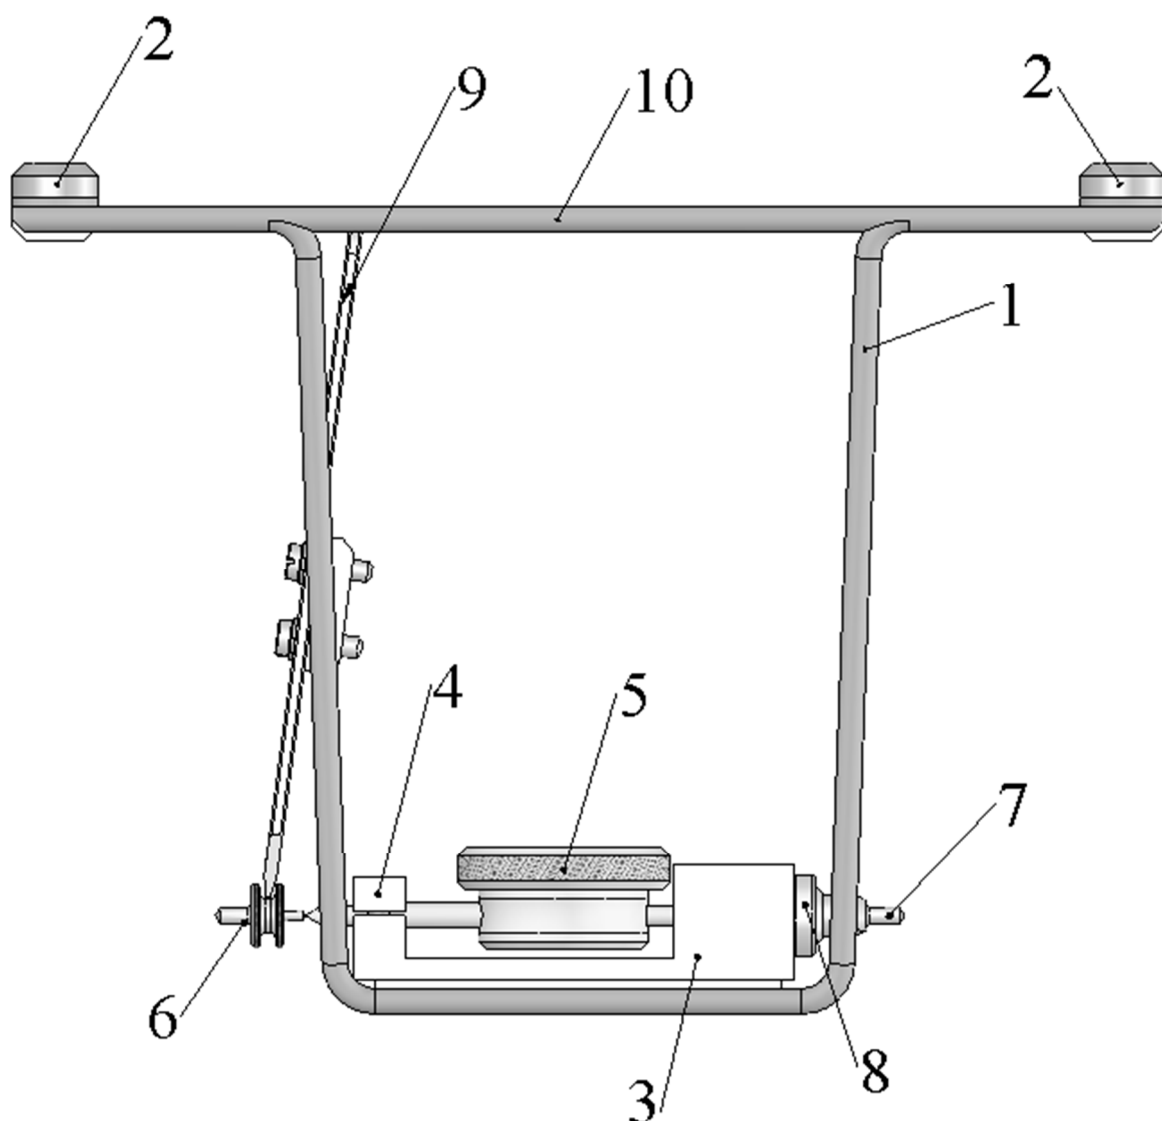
Типовая конструкция индикаторного прибора для измерения диаметра уплотнительной расточки муфты на заданном расстоянии от упорного уступа: 1 – держатель; 2 – ручки; 3 – корпус; 4 – зажимная планка; 5 – индикатор; 6, 7 – сменные измерительные наконечники; 8 – гайка; 9 – арретир; 10 – перемычка.
